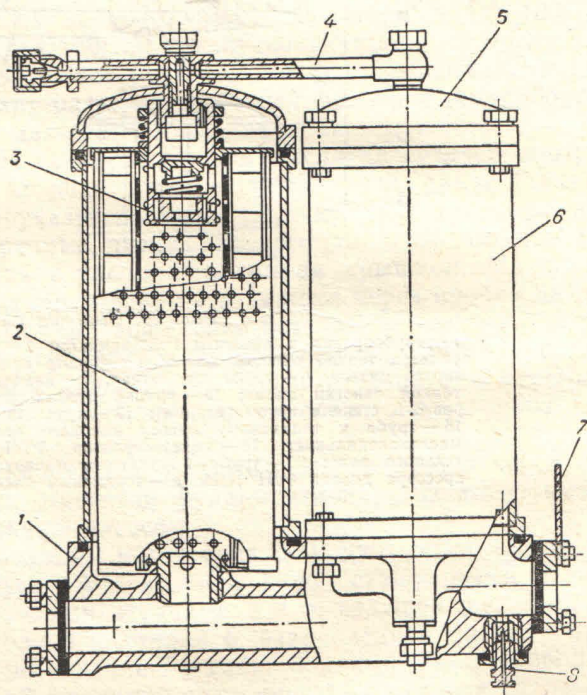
Полнопоточный фильтр тонкой очистки масла: 1 — основание корпуса; 2 — фильтроэлемент; 3 — клапан перепускной; 4 — трубка дренажная; 5 — крышка; 6 — корпус; 7 — предупредительная табличка; 8 — пробка
